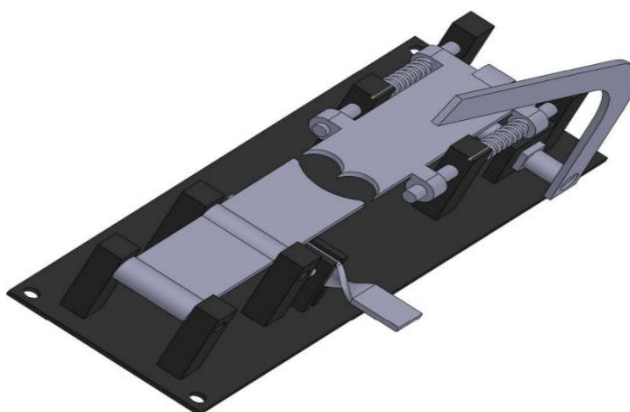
Vue 3D du dessin d'ensemble de la décortiqueuse
